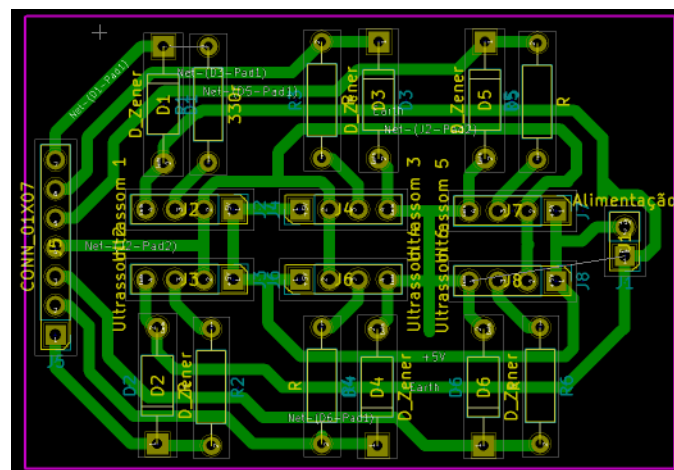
PCB do circuito eletrônico para os sensores ultrassom.
